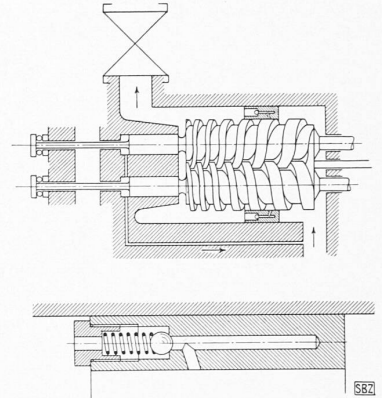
Auslassventil im Scheibenkolben der Schraubenpumpe nach System F. X. Zerr
